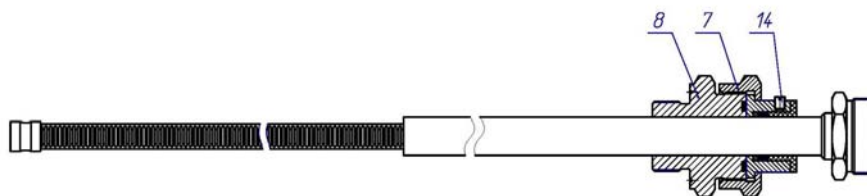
Расположение внешнего корпуса горизонтально на поверхности
